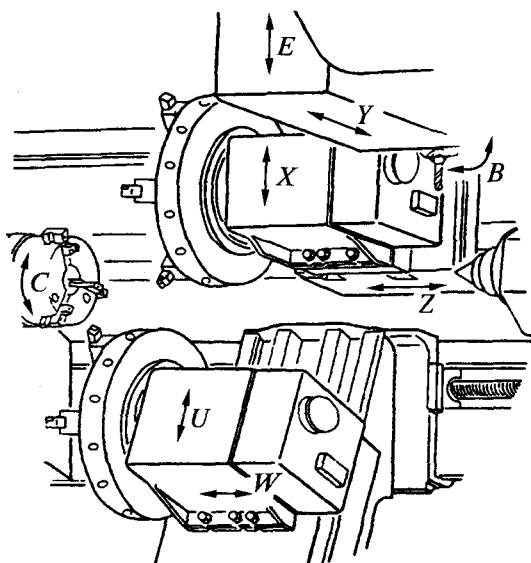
Компоновка рабочего пространства обрабатывающего центра «Voest-Alpine»
